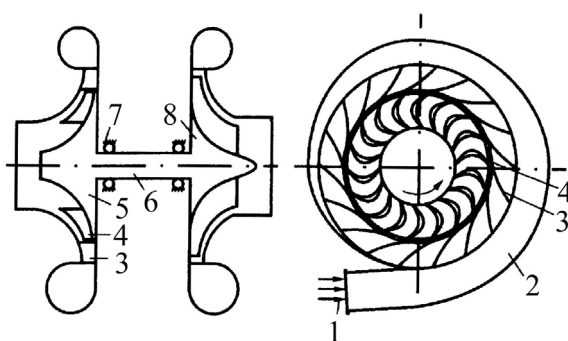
Схема работы турбохолодильника с двухступенчатым расширением: 1 — патрубок; 2 — улитка; 3 — сопло; 4 — лопатки рабочего колеса; 5 — рабочее колесо турбины; 6 — вал; 7 — подшипник; 8 — колесо вентилятора [9]
